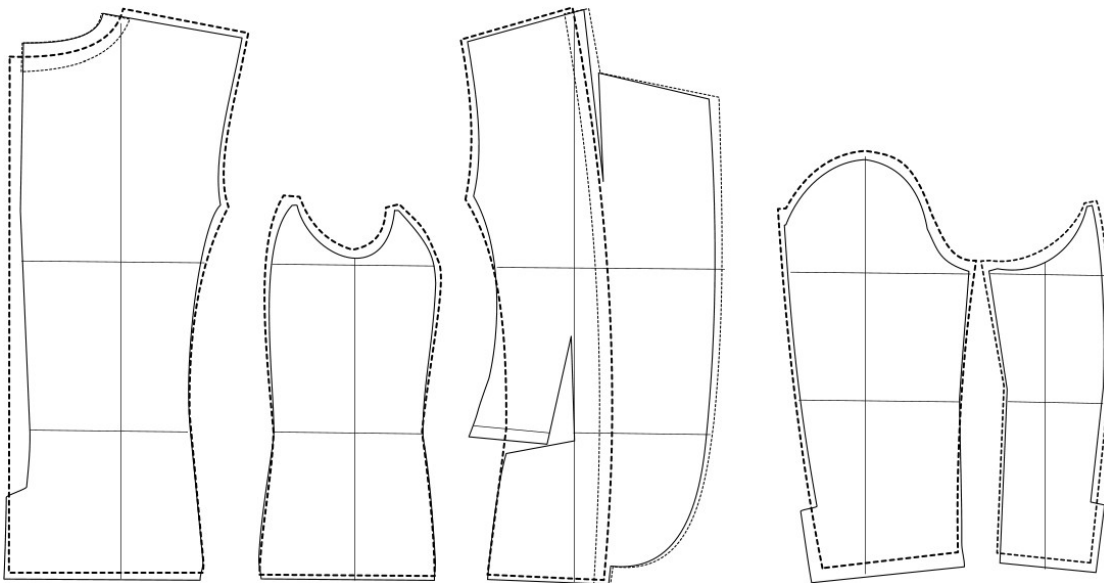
Схема побудови похідних лекал деталей з підкладки
